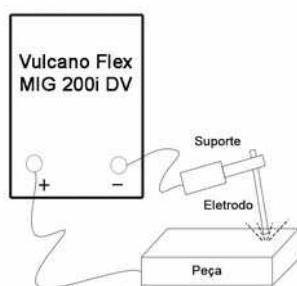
Conexão negativa para soldagem com eletrodo revestido
